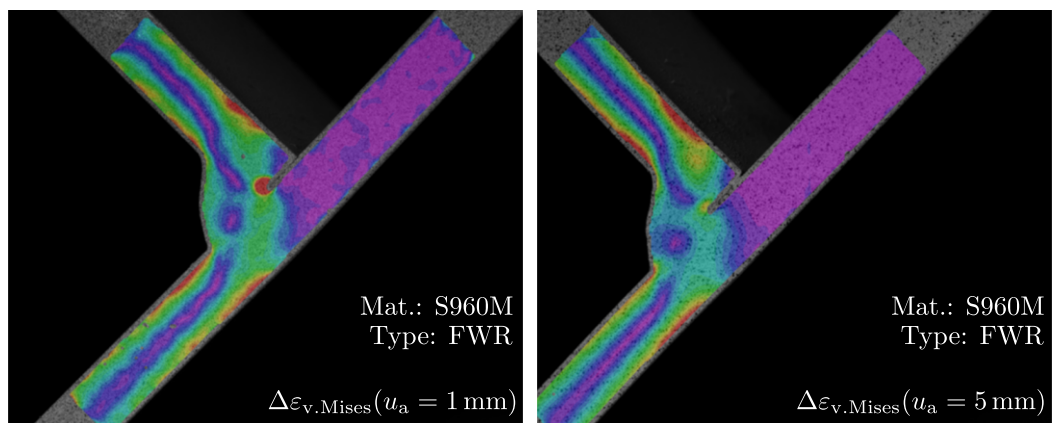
Gemessene Dehnungsfelder für nicht durchgeschweißte T-Stöße aus S960M.
